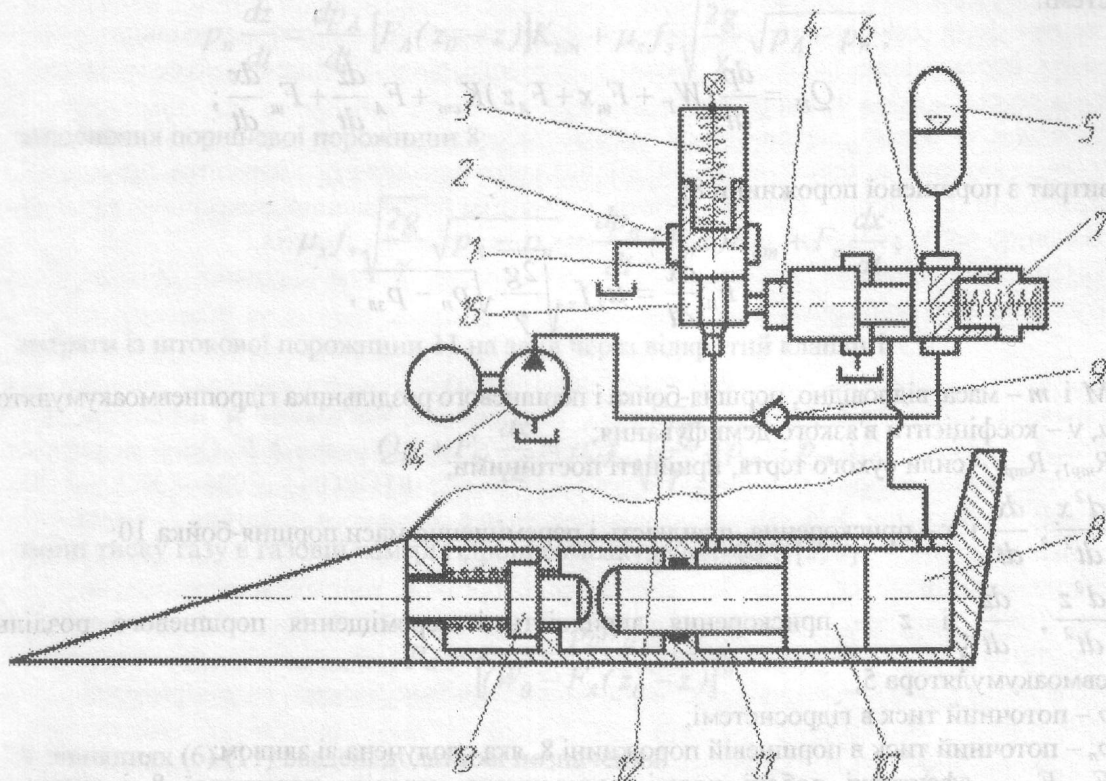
Принципова схема ударного вузла ковпа активної дії
